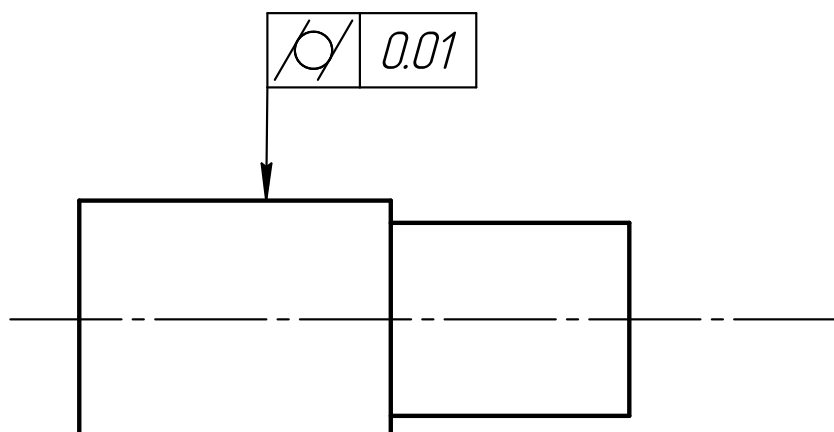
Обозначение на чертежах допуска цилиндричности
